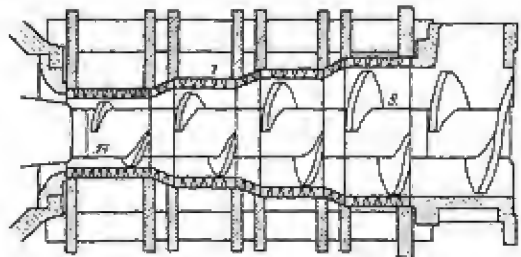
Schnitt durch die Schneckenpresse der FRIEDR. KRUPP GRÜNDUNGWERK A. G., Magdeburg.
